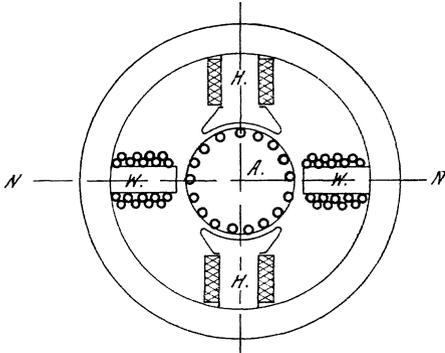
Motorgehäuse mit Feldmagneten *H.* und Wendepolen *W.
